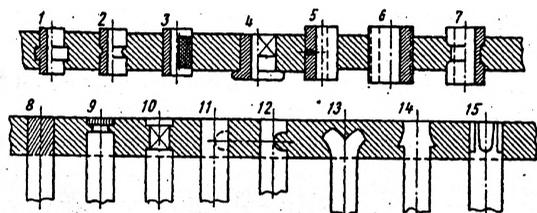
Варианты изготовления заливаемой части арматуры: 1 - внешний бортик; 2 - кольцевой паз; 3 - крестовая накатка; 4 - разделка на квадрат и бортик; 5 - отверстия; 6 - резьба; 7 - выточка; 8 - косая накатка; 9 - заточка с прямой накаткой; 10 - разделка на квадрат; 11 - сверление; 12 - прорезка; 13 - раздвоение конца; 14 - насечка; 15 - скосы.
